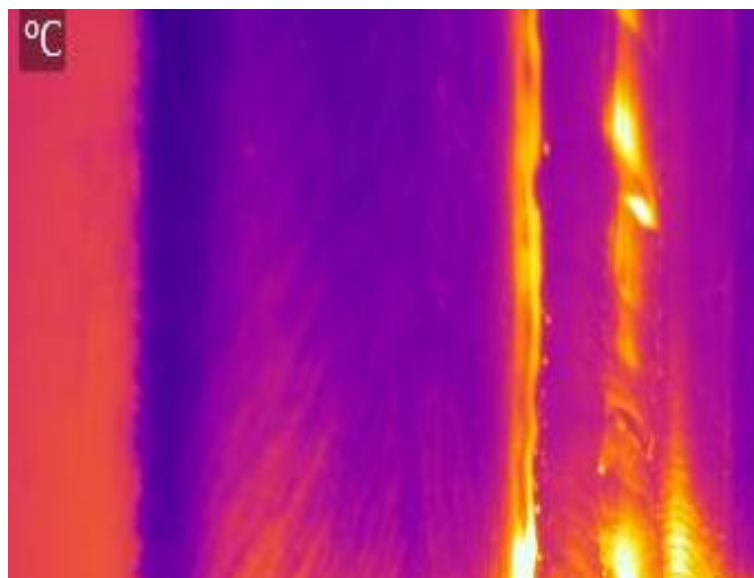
Proyecciones de soldadura agrupadas.
